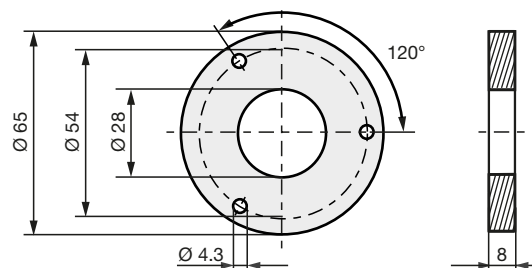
Accessori speciali BTL-P-1028-15R
